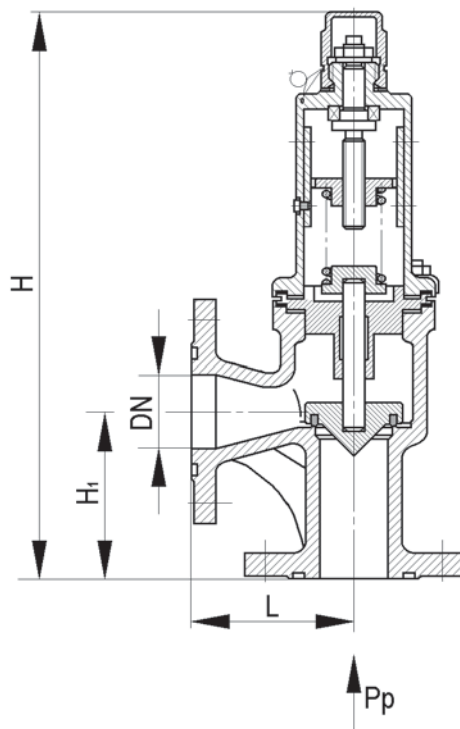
Клапан предохранительный угловой фланцевый
